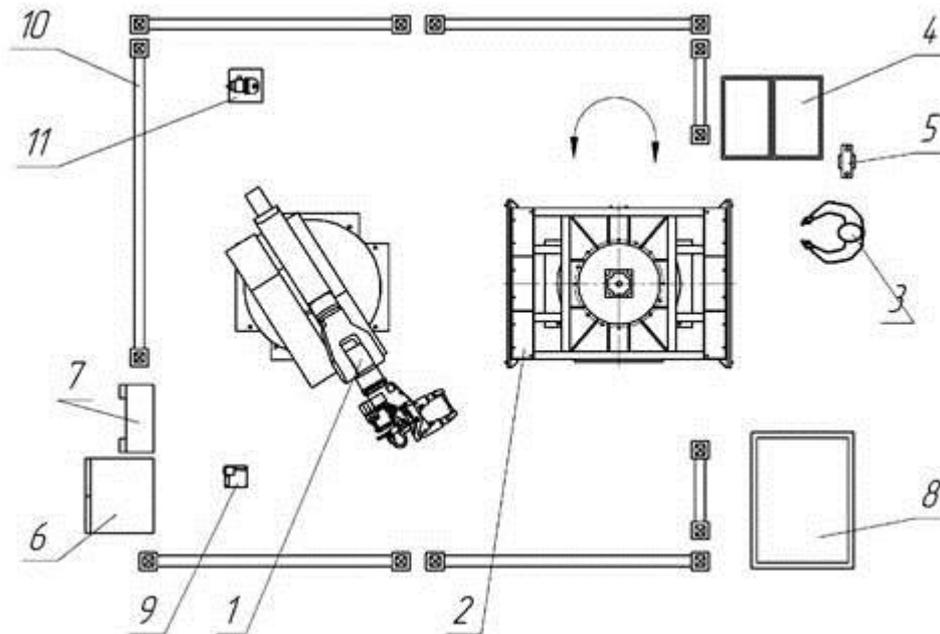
РТК для контактной точечной сварки с одним сварочным роботом
